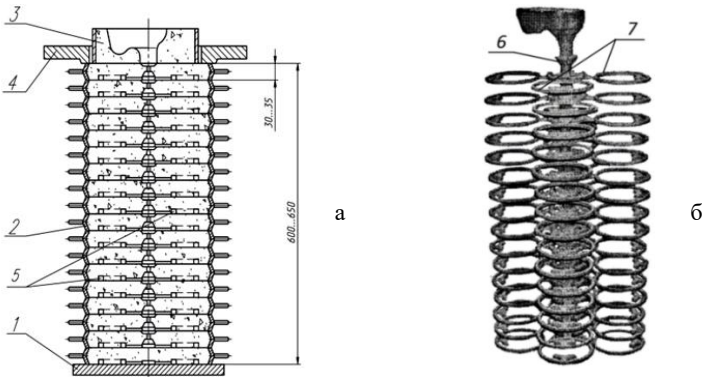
Вертикальна стопкова форма (стопа) для лиття кілець-заготовок поршневих кілець (а) [13]: 1 – піддон; 2 – опока; 3 – заливальна чаша; 4 – вантаж; 5 – порожнина під виливку заготовки поршневого кільця; 6 – стояк литникової системи; 7 – куц виливків заготовок поршневих кілець після вибивання зі стопи (б) [14].
